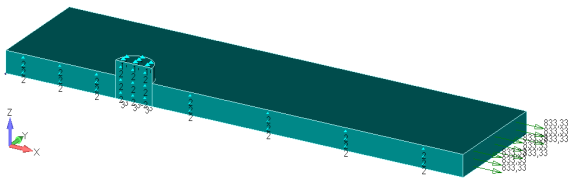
Розрахункова модель пластини у контакті з циліндром ("болтом")
